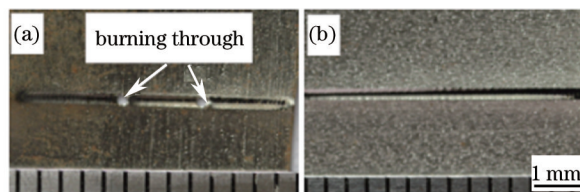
典型焊缝表面形貌。(a) 图2(a)焊缝; (b) 图2(b)焊缝
